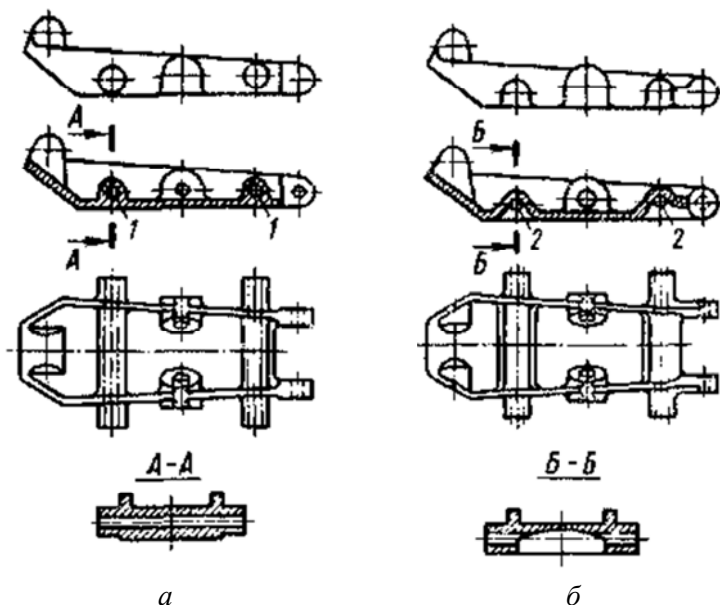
Конструкция отливки из алюминиевого сплава:
